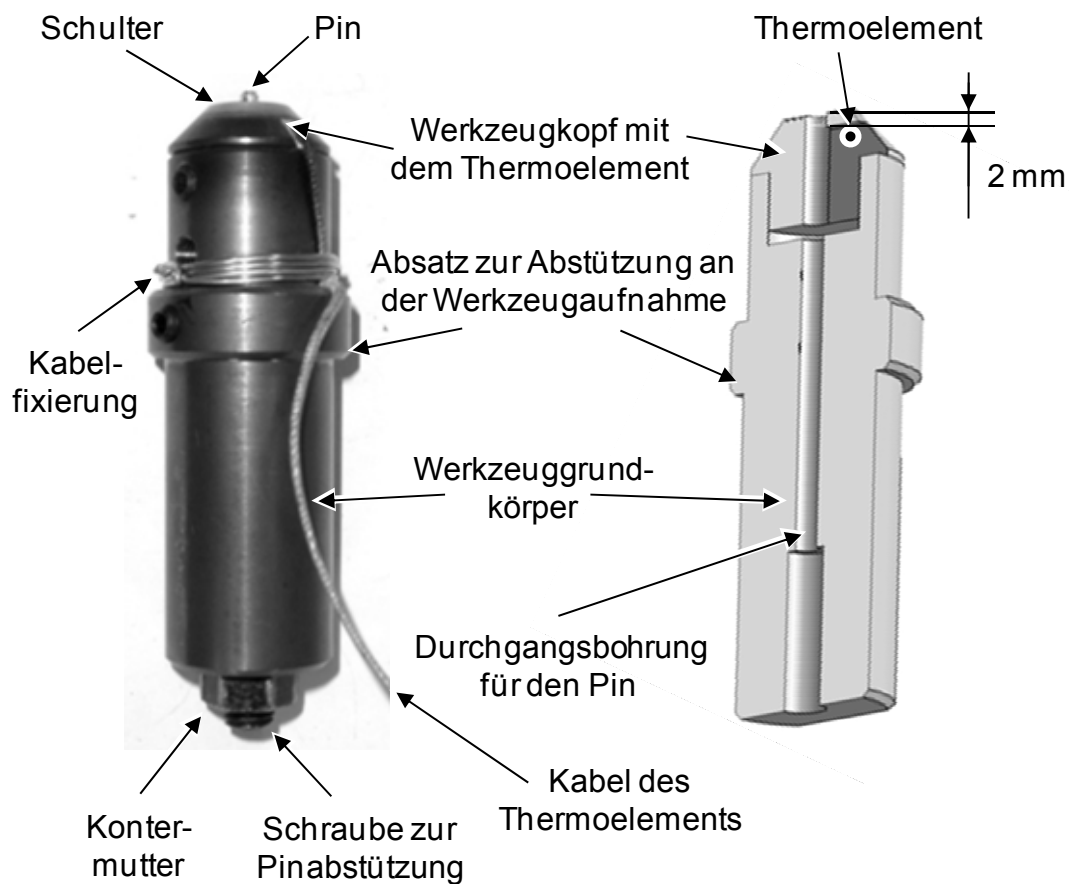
Foto des FSW-Werkzeuges mit integriertem Thermoelement und Querschnitt durch das CAD-Modell in der Ebene der Werkzeugachse
